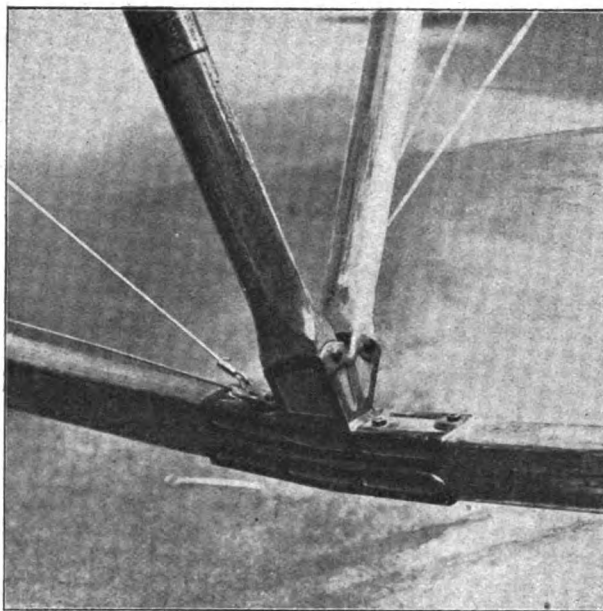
Verbindung der Kufe mit 2 Streben beim Zweidecker „Doutre“.
